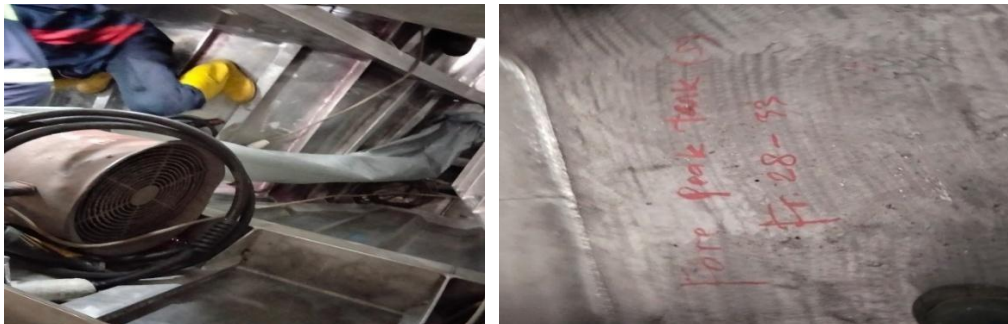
pengecekan welding pada aft peak tank
